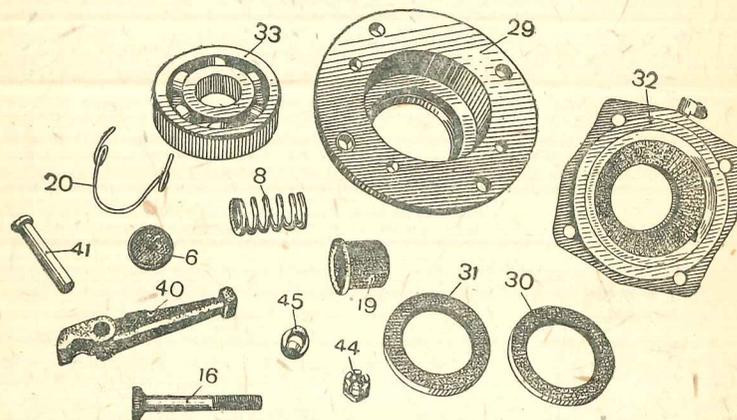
Детали отжимного рычага и заднего подшипника муфты сцепления.
